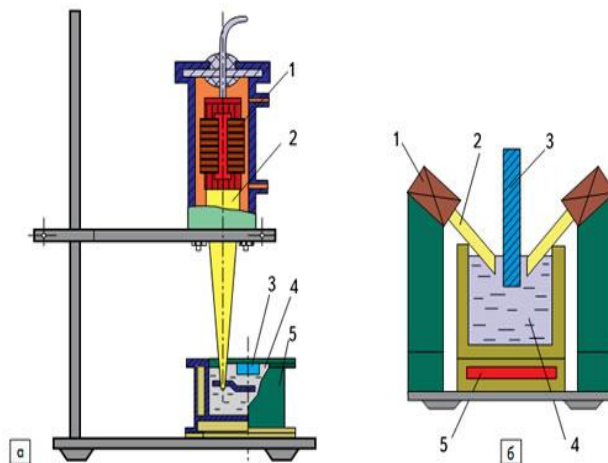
Схемы локального ввода ультразвука в расплав: а) одним излучателем; б) двумя излучателями: 1 — преобразователь; 2 — волновод; 3 — деталь; 4 — припой; 5 — нагреватель
